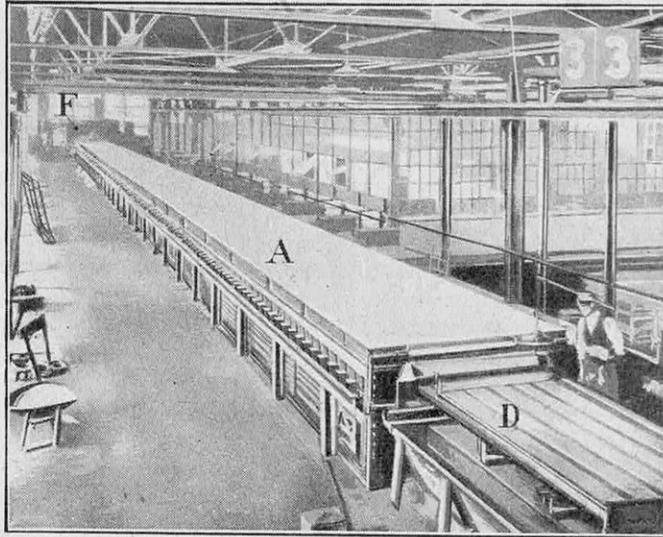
VUE D'ENSEMBLE D'UN HALL D'ÉTIRAGE POUR LA FABRICATION MÉCANIQUE DU VERRE A VITRE (PROCÉDÉ LIBBEY-OWENS)
